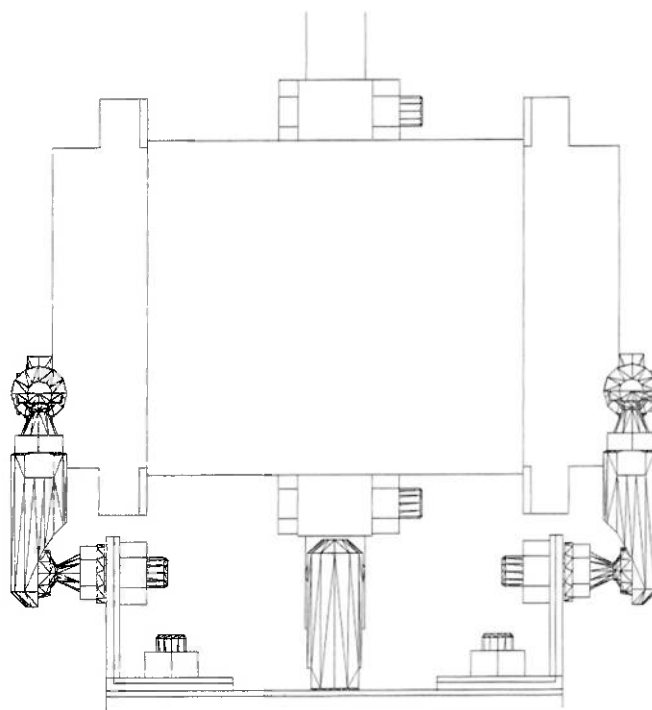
Desenho de conjunto do tornozelo – vista isométrica
